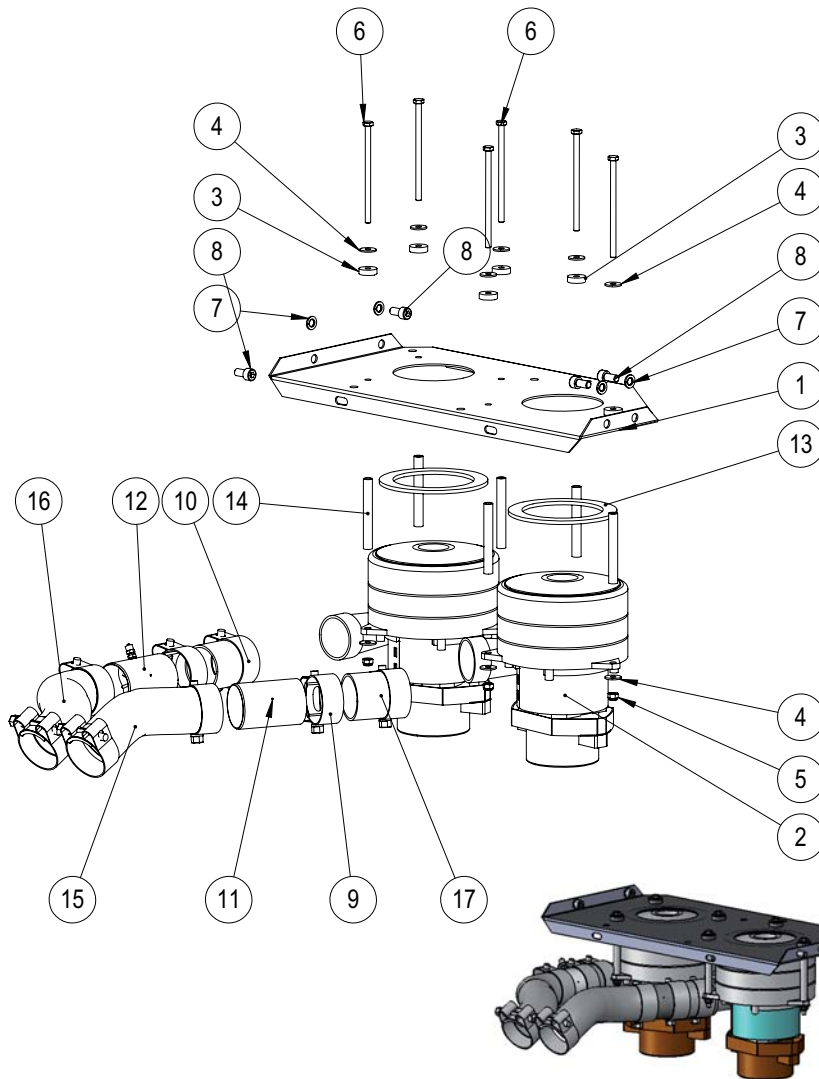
Explosionszeichnung Maschinenaufbau M95 400V 5,5kW
